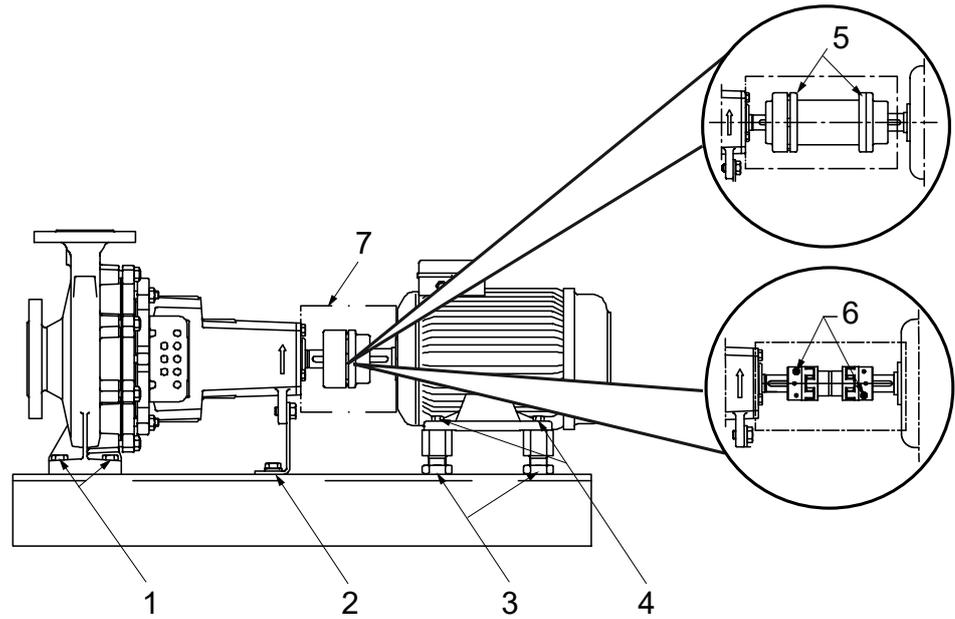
Posiciones de apriete de los tornillos del grupo motobomba
